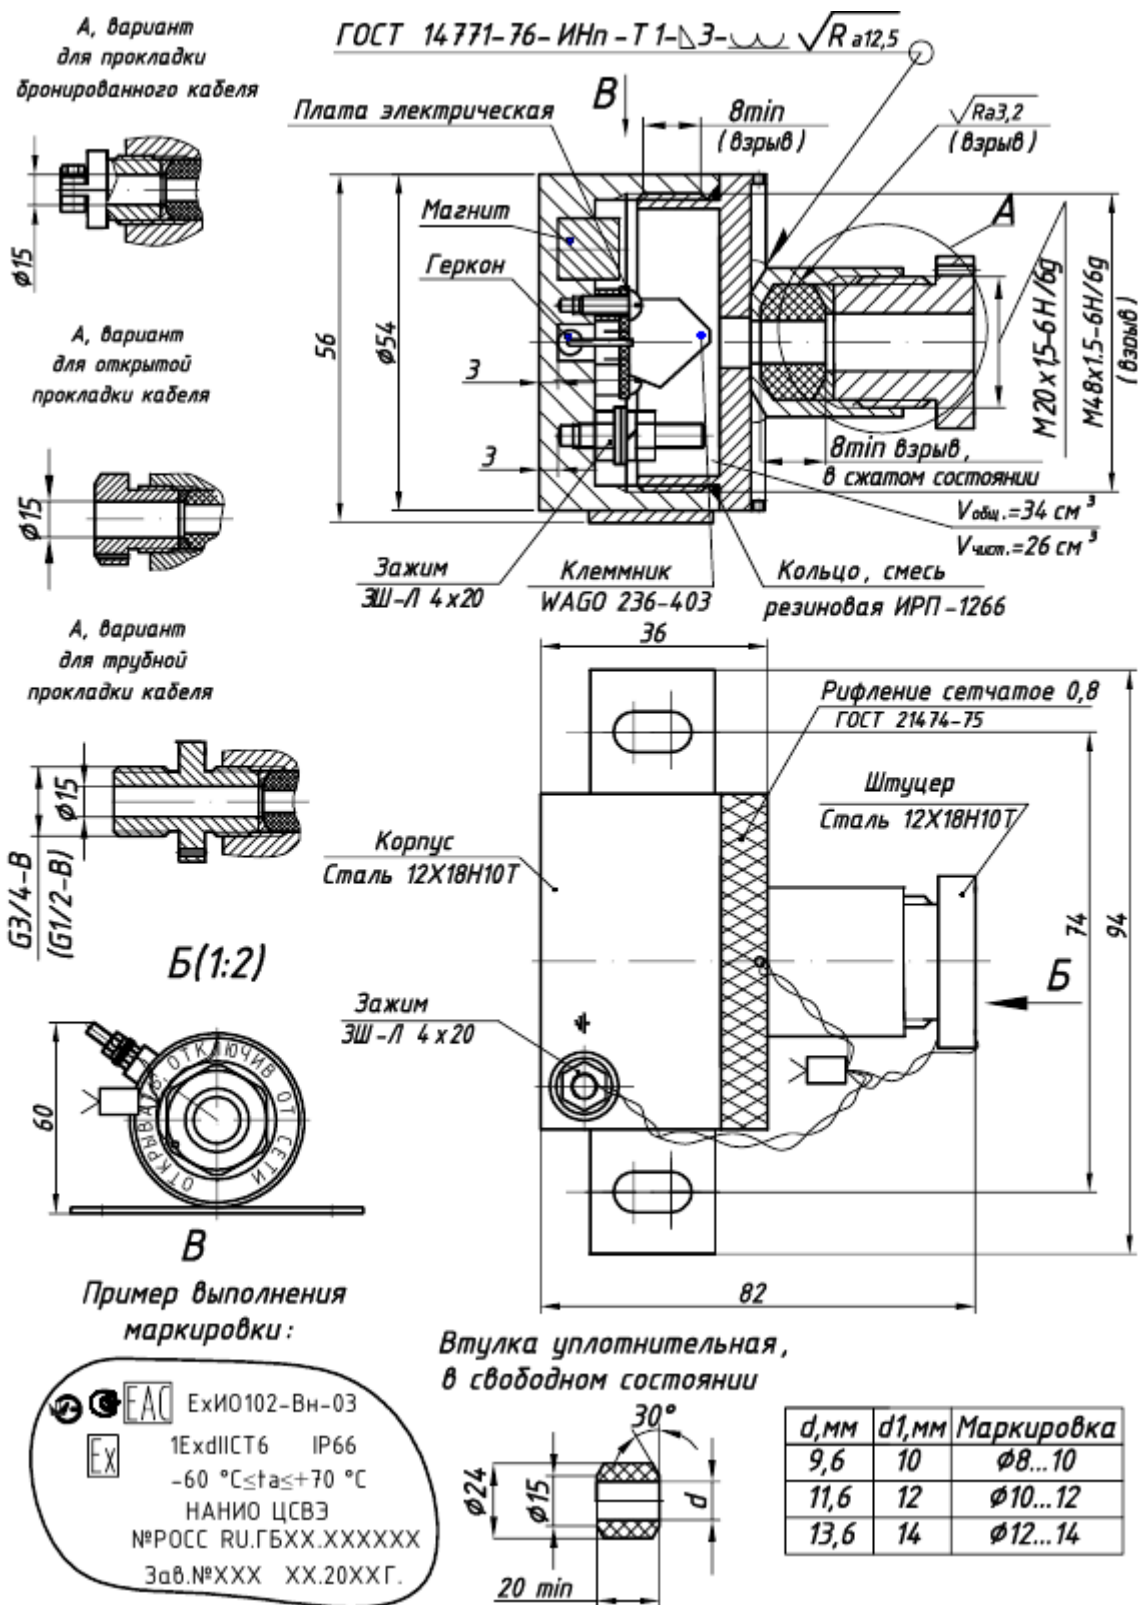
Габаритный чертёж Извещателей моделей 03 с элементами взрывозащиты.
